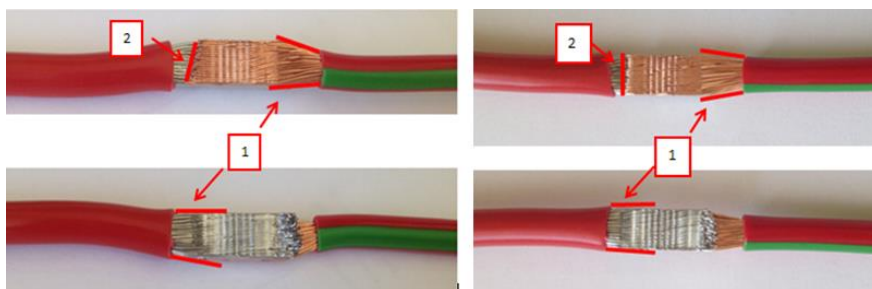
Lado esquerdo exemplo de soldadura com cabos desalinhados; lado direito exemplo de soldadura com cabos alinhados
